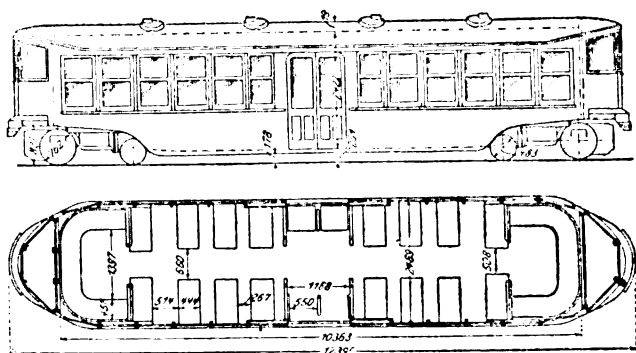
Vettura tramviaria di New York. - Elevazione e pianta.
